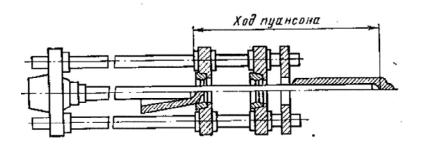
Схема штампа для вытяжки поковки на горизонтальном прессе
